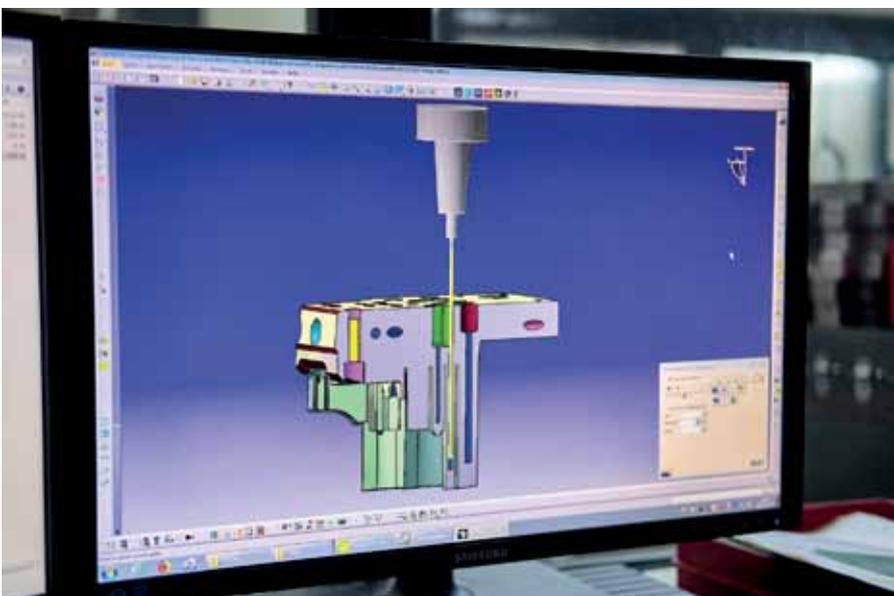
Bohraufgabe für den 113-HP in einem Spritzgusswerkzeug für ein Enthärtermittelteil.
